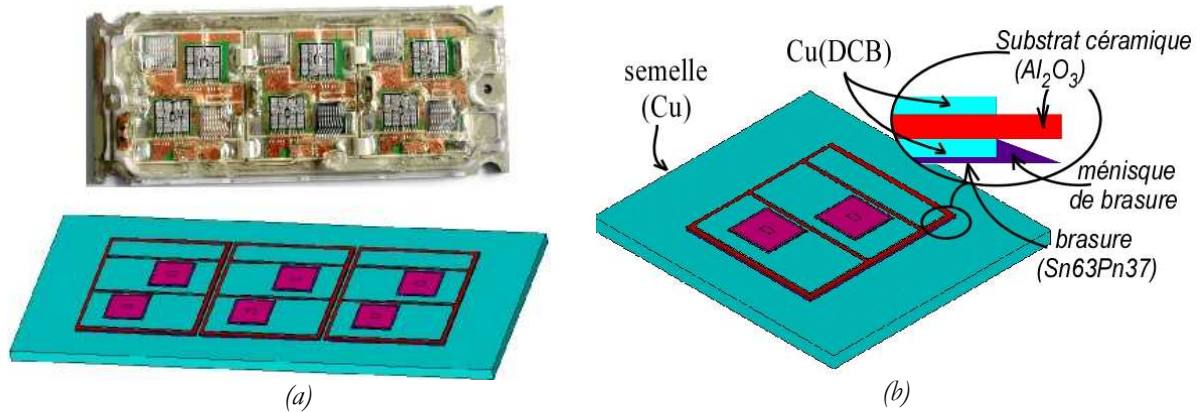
Modèle 3D du module entier (a) et d'un seul DCB (b)
